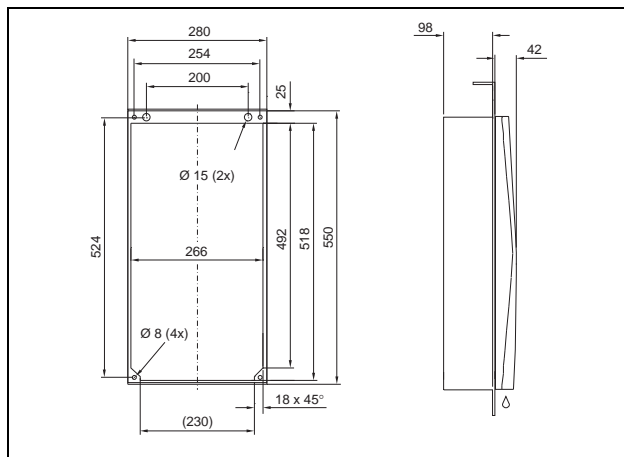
SK 3332.xxx, pro částečné zapuštění
